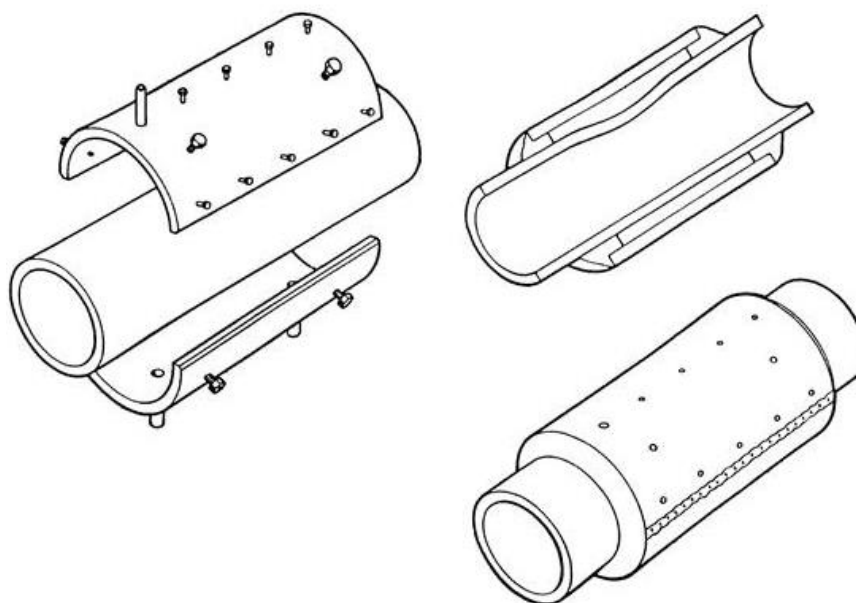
Ремонтная муфта со сварным соединением полумуфт
